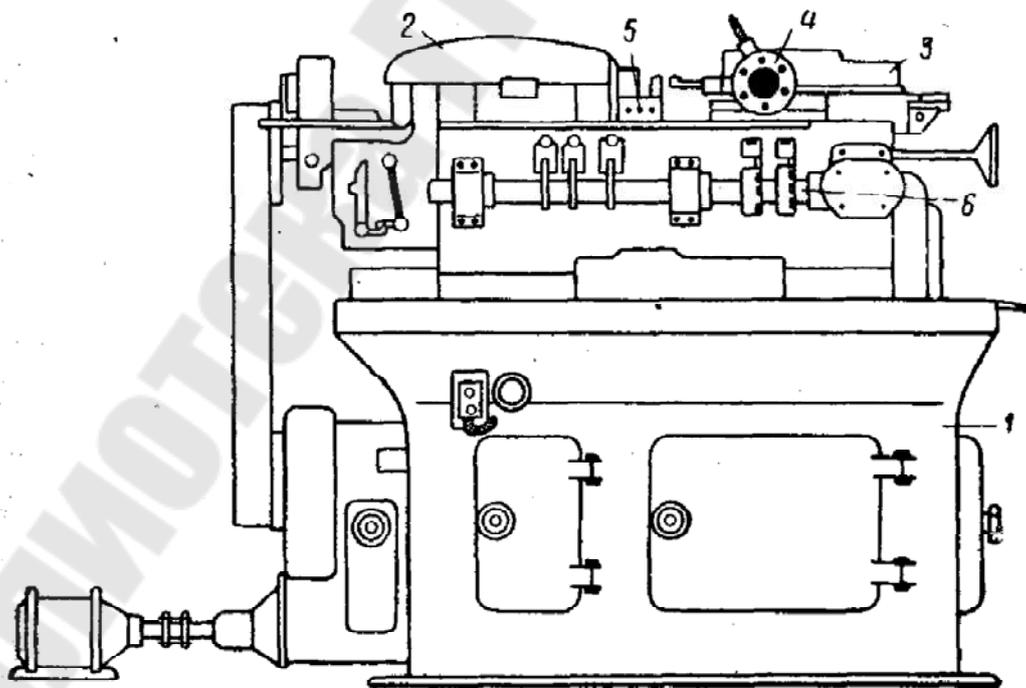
Эскиз общего вида токарно-револьверного автомата модели 1112
